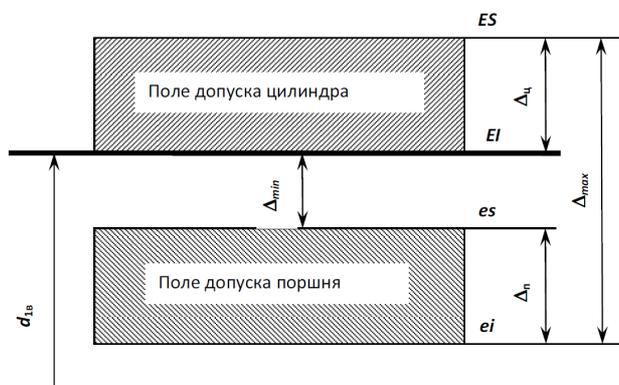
Схема расположения полей допусков сопряжения поршня и цилиндра силового гидроцилиндра
